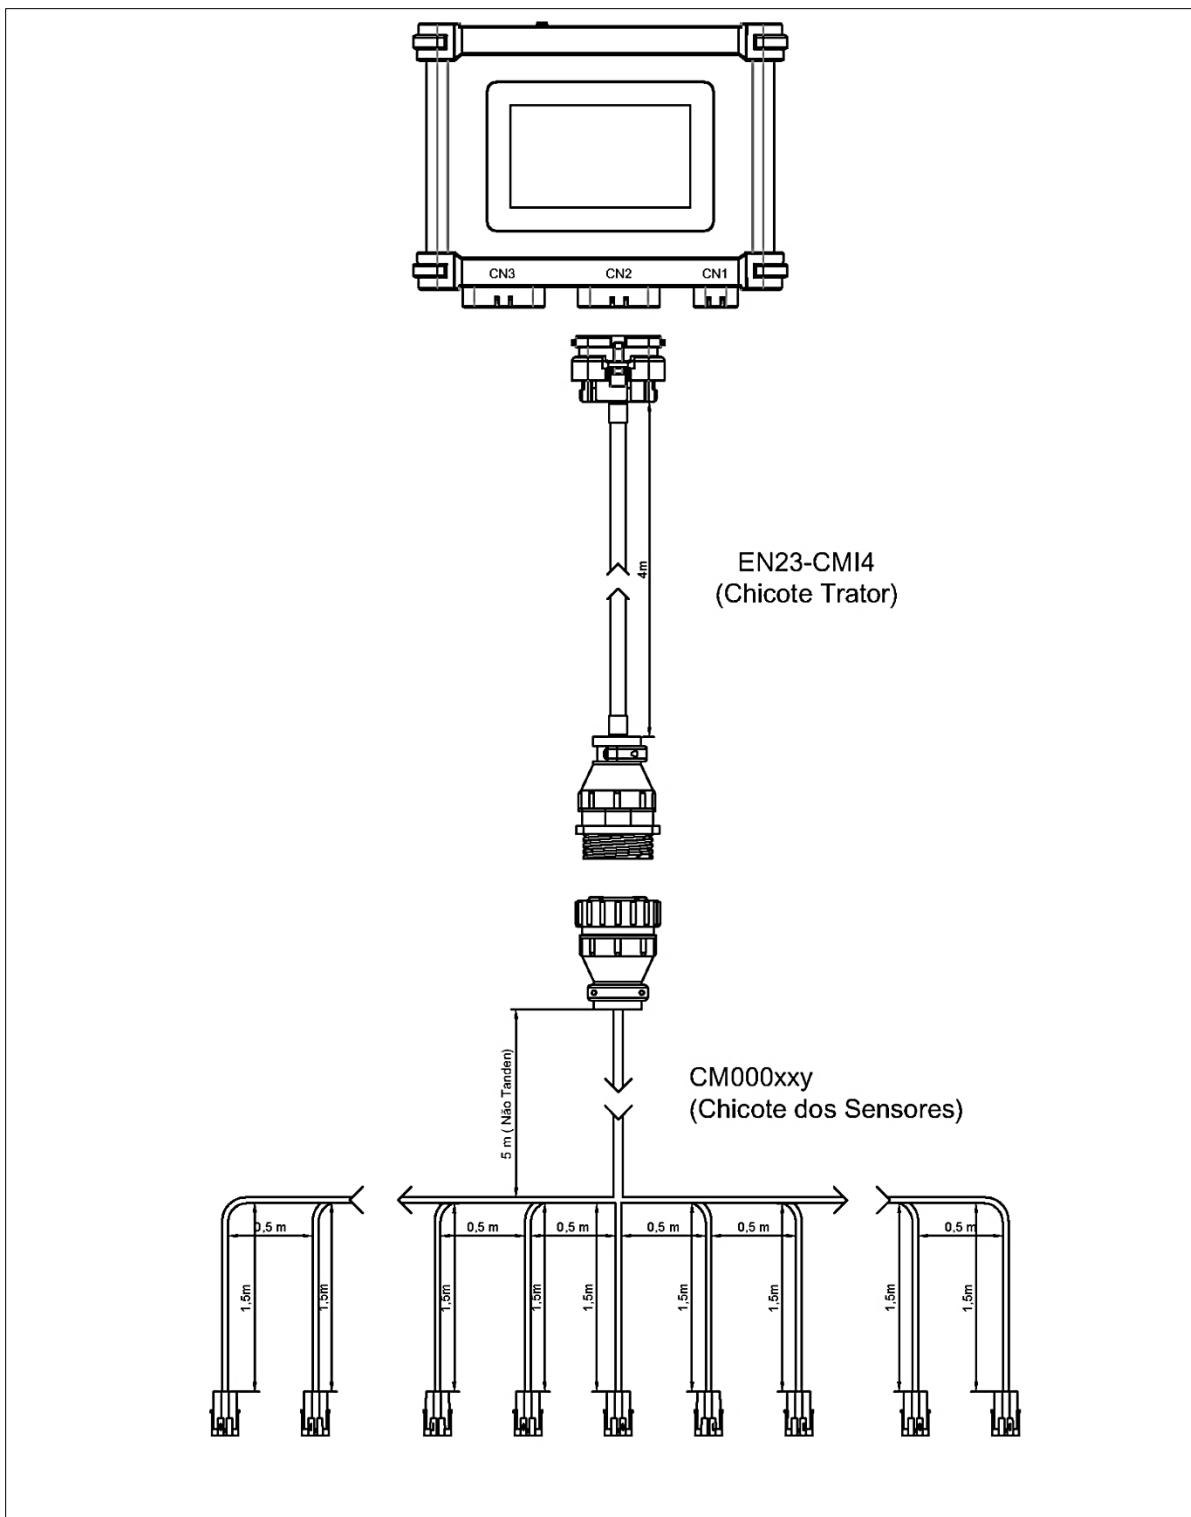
Esquema de montaje para implementos de plantación en configuración no tandem
